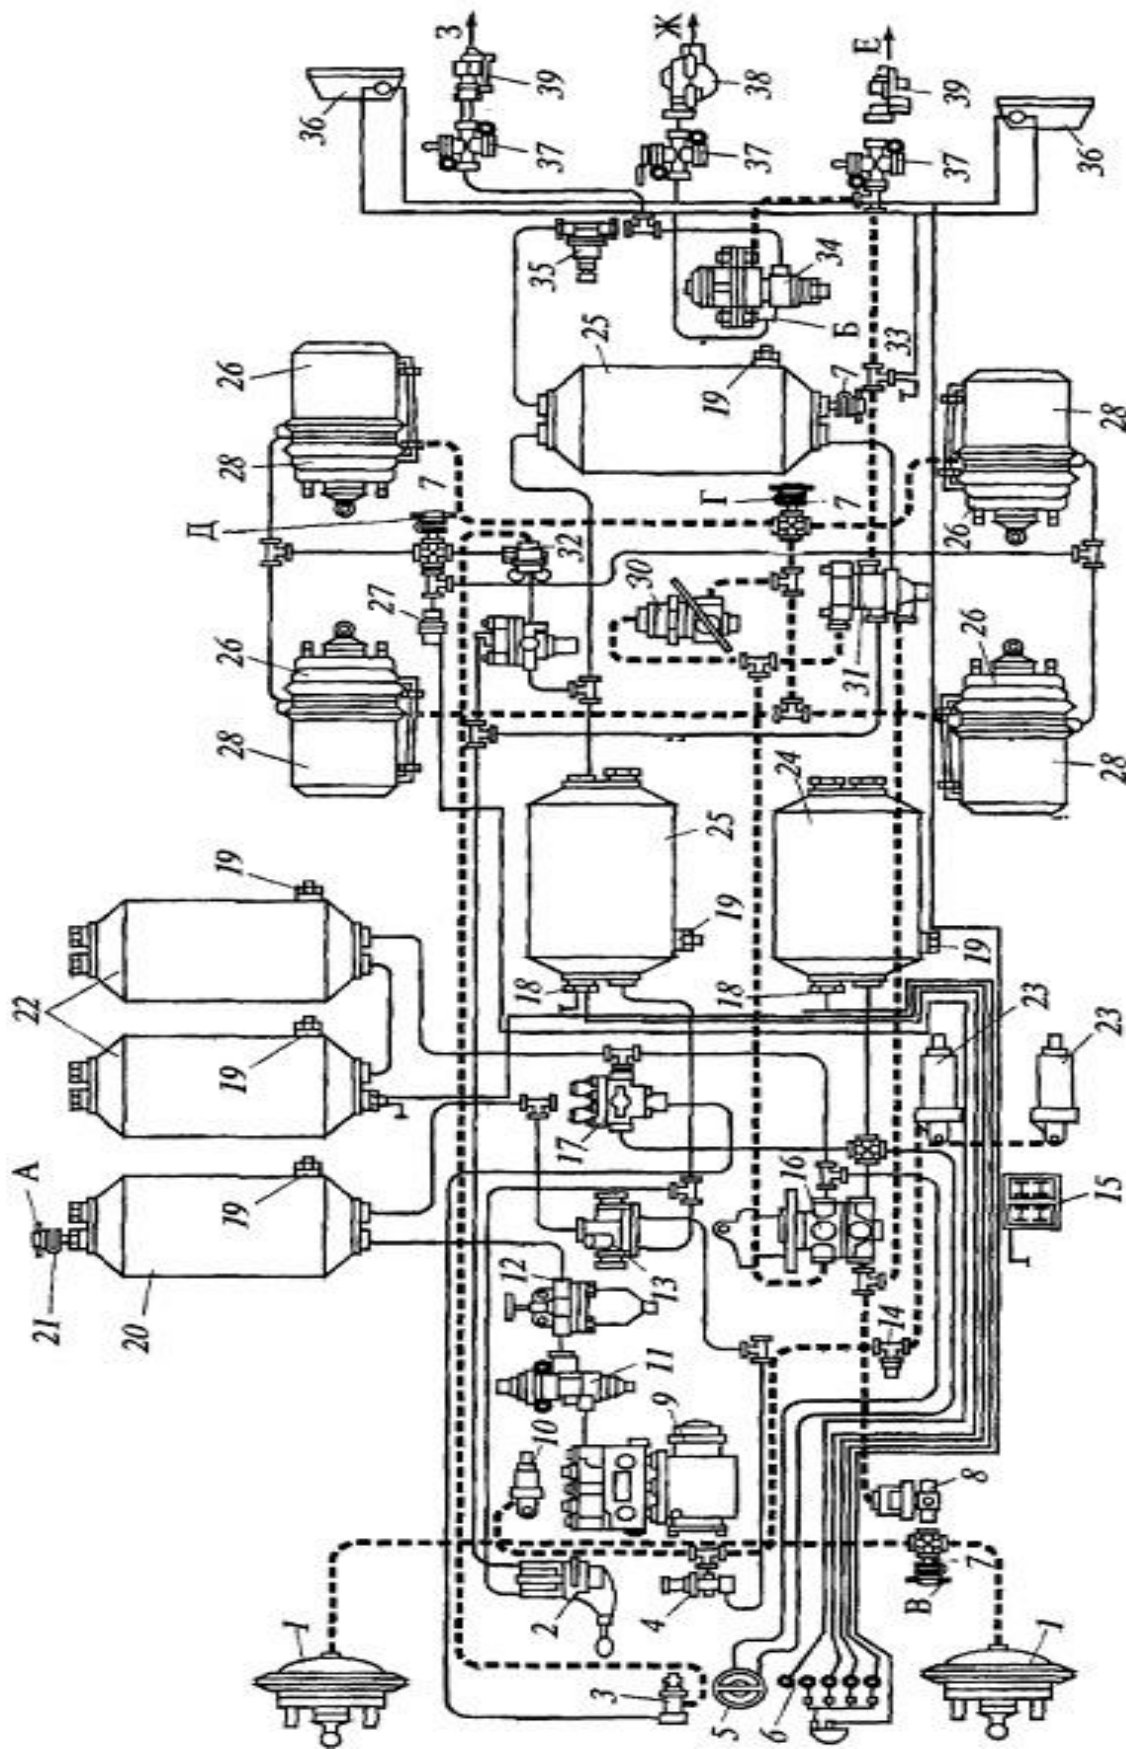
Схема пневматического тормозного привода автомобиля КамАЗ
